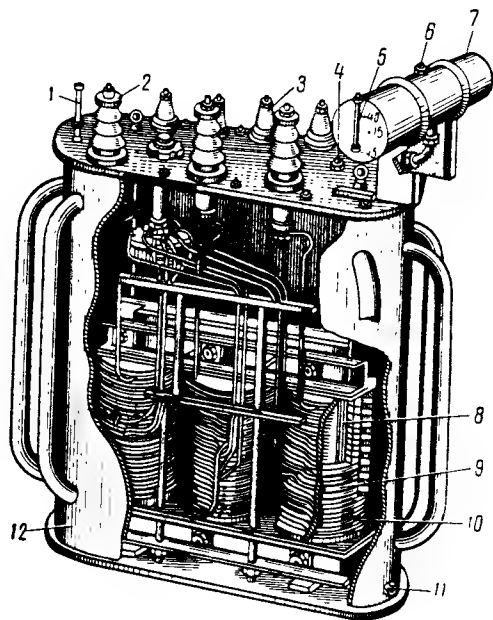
Общий вид силового масляного трехфазного трансформатора мощностью 320 кВа, 6 кВ, с трубчатым баком: 1 — термометр; 2 — ввод обмотки ВН; 3 — ввод обмотки НН; 4 — пробка для заливки масла; 5 — указатель уровня масла; 6 — пробка для доливки масла; 7 — маслорасширитель; 8 — магнитопровод; 9 — обмотка НН; 10 — обмотка ВН; 11 — пробка для взятия пробы и спуска масла; 12 — бак для масла
